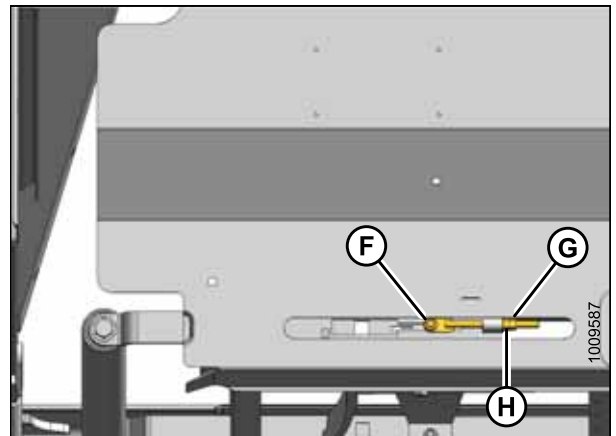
Rodillo tensor de la plataforma izquierda (se muestra a la izquierda, derecha opuesta)
